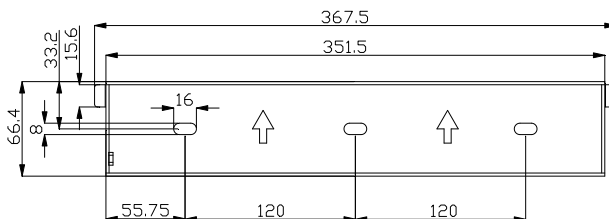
Dimensões do suporte de apoio do R5-7K/8K-S2
